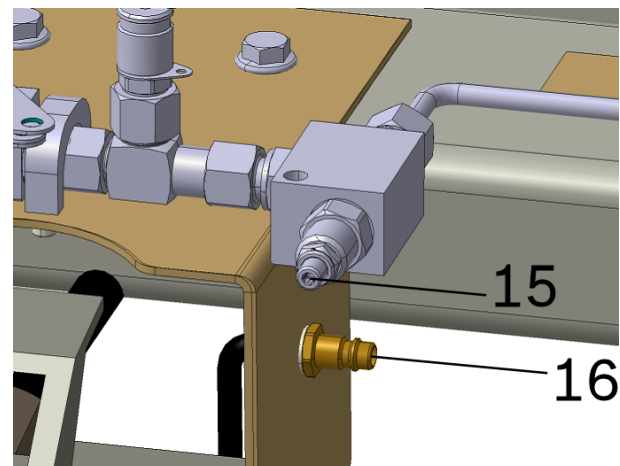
Hydraulisches Überdruckventil, Detailansicht
